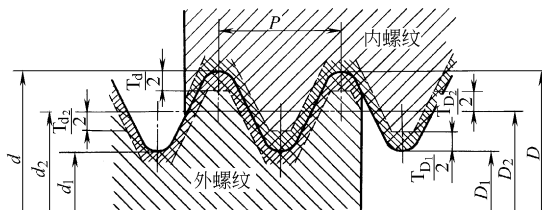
55°非密封圆柱管螺纹基本尺寸及公差带
